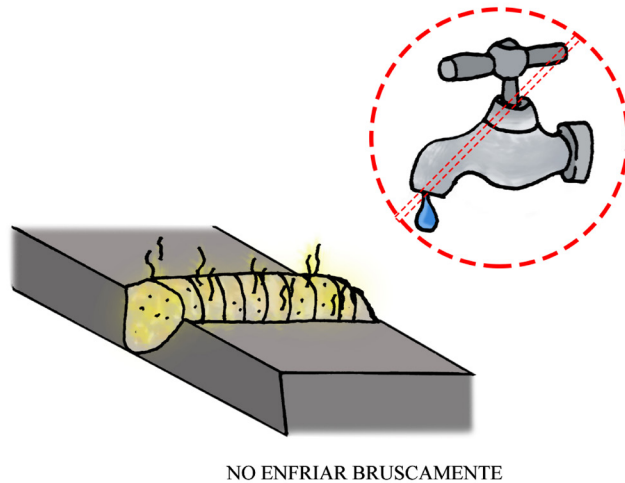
No enfriar bruscamente las piezas al terminar la soldadura.
